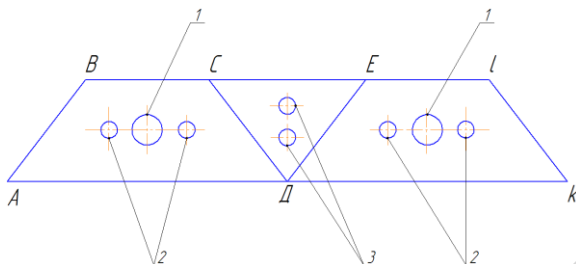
Предлагаемая полевая доска корпуса плуга (патент № 19151)
